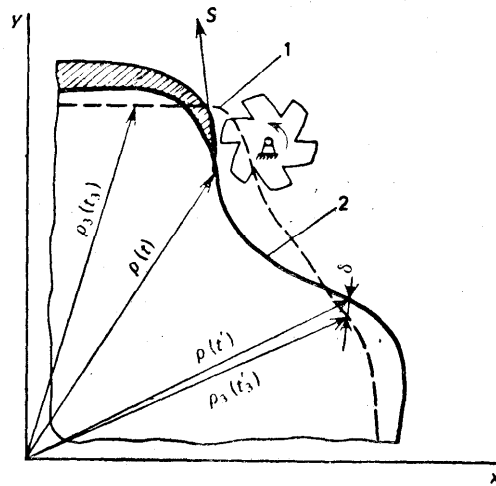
Схема фрезерования детали на станке с ЧПУ:
